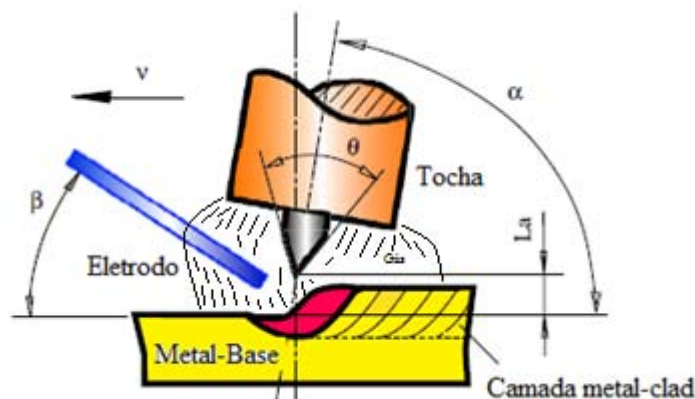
Esquema de soldagem sobre camada usando o processo TIG. Adaptado de Xu [38].
